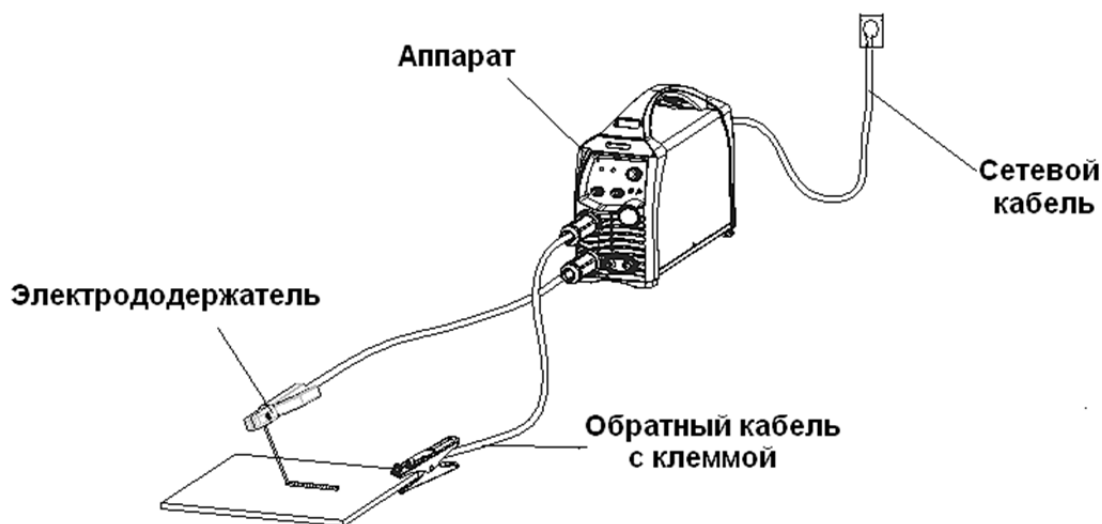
Схема подключения оборудования для ММА сварки
